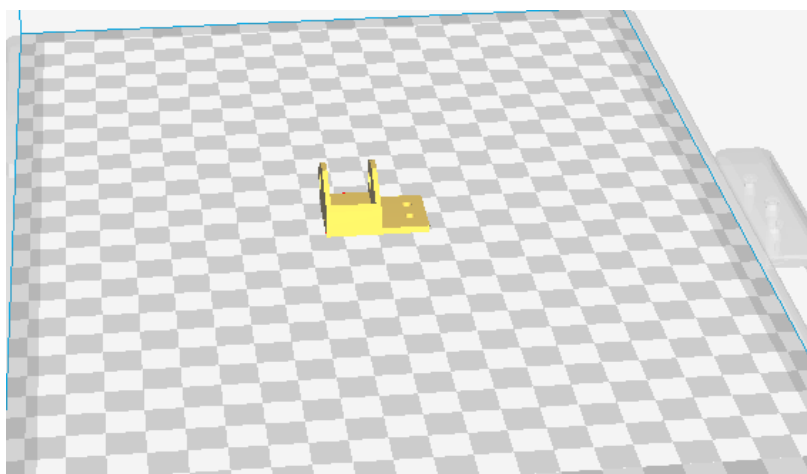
Posición de impresión del acoplador 2 de cadena.
